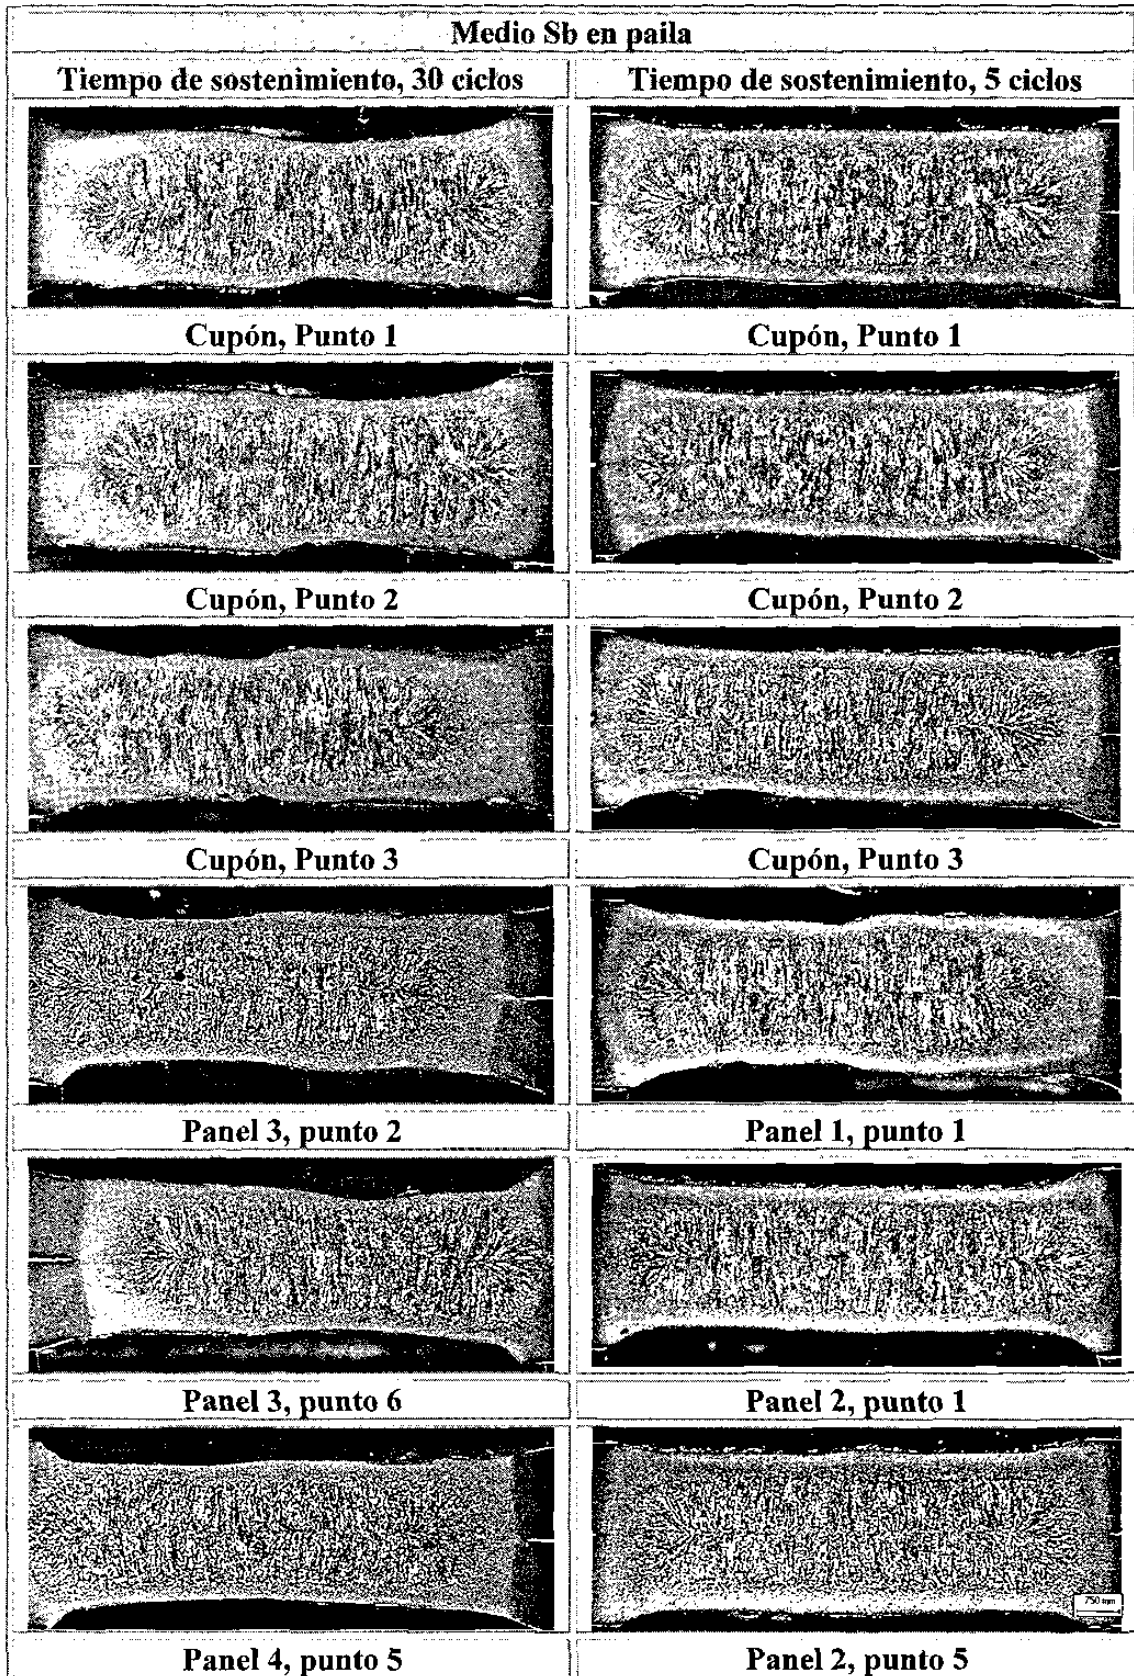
Sección transversal del botón de soldadura para la prueba de medio Sb.
